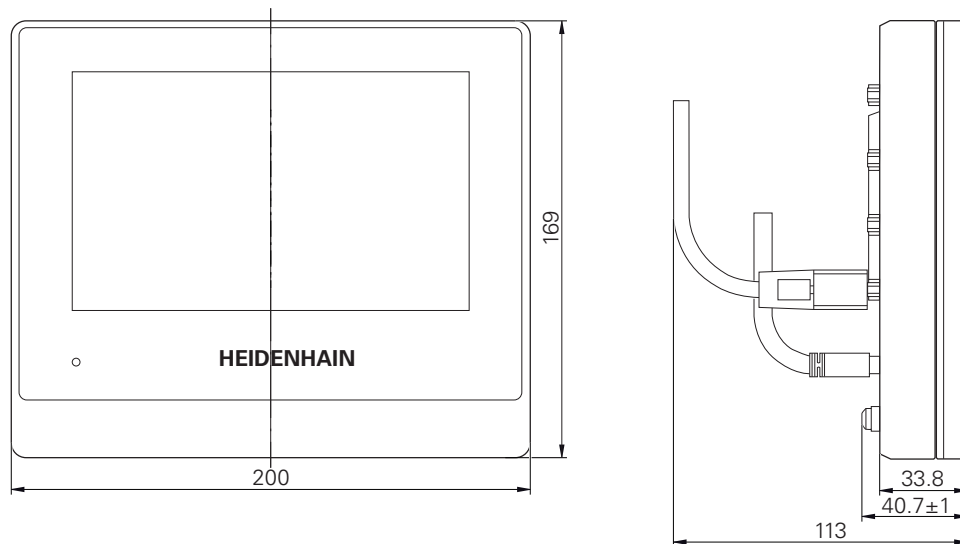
Dimensionering av huset till enheterna med ID 1089178-xx
